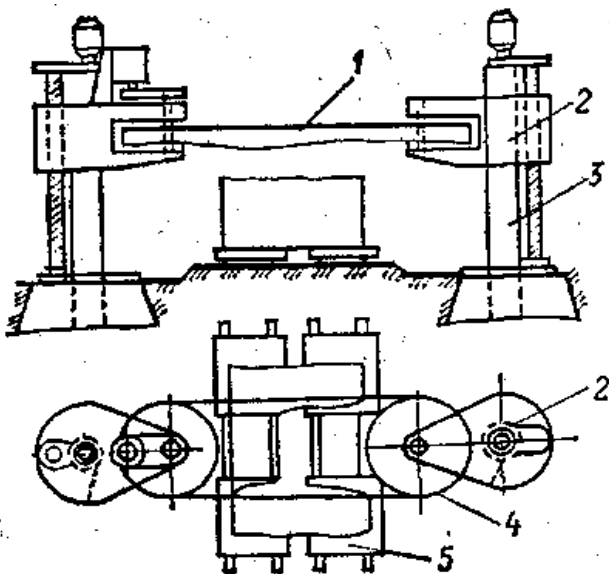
Принципова схема стрічкопильного верстата. Позначено: 1 – станина; 2 – привод виконавчого органа; 3 – привод механізму робочої подачі; 4 – виконавчий орган; 5 – робочий стіл [30].
